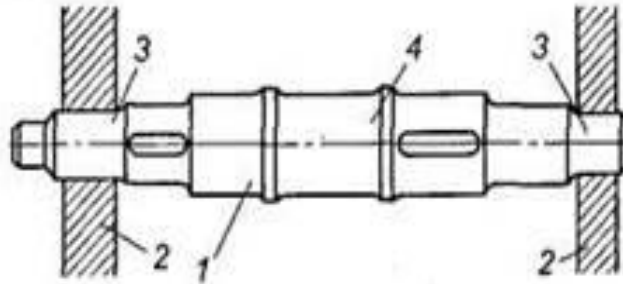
Схема работы ступенчатого вала: 1 — ступенчатый вал; 2 — опоры вала; 3 — цапфы; 4 — шейка
